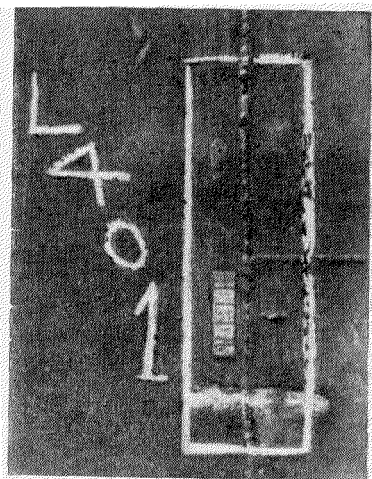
Сварной шов, подготовленный к просвечиванию γ -лучами.
